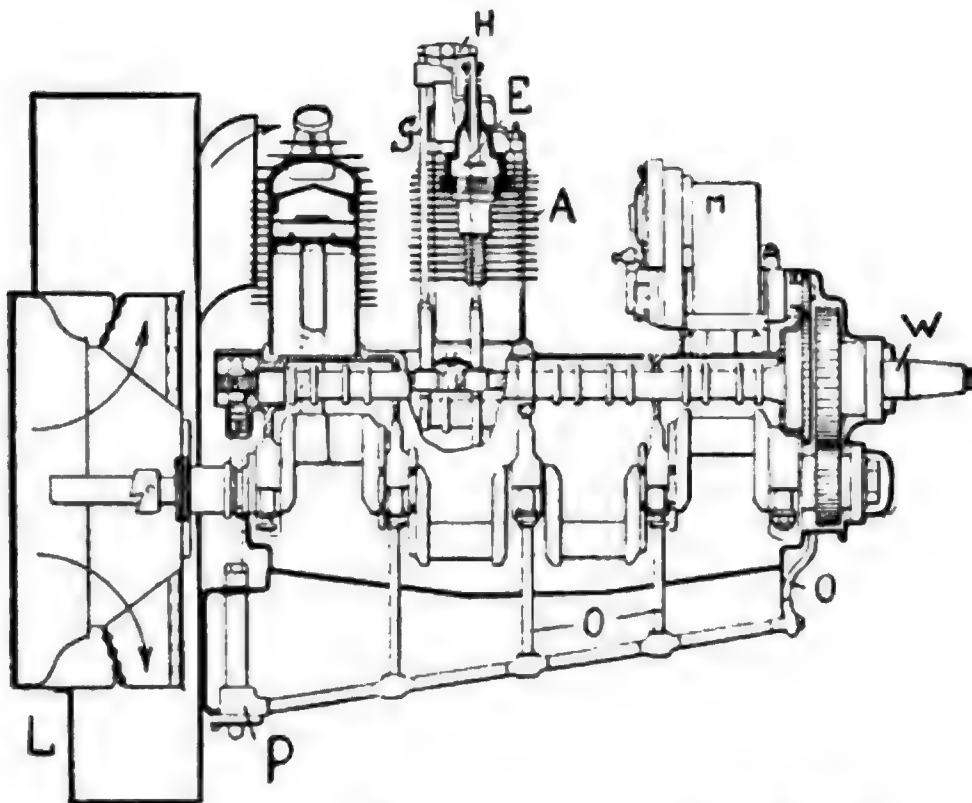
Luftgekühlter Flugmotor von Renault Frères. Längsschnitt.
